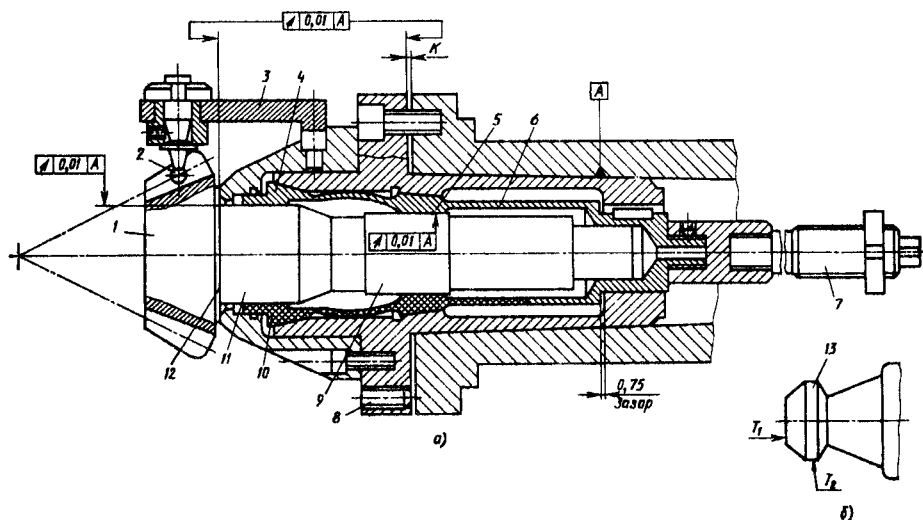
Зажимное приспособление для обработки колеса-вала:
